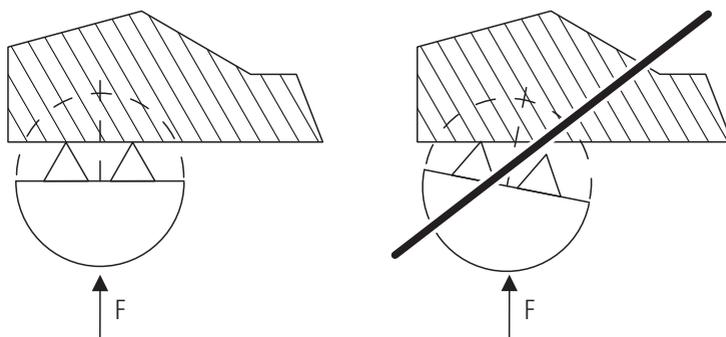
Упорные центры GRIPP на обрабатываемой детали
